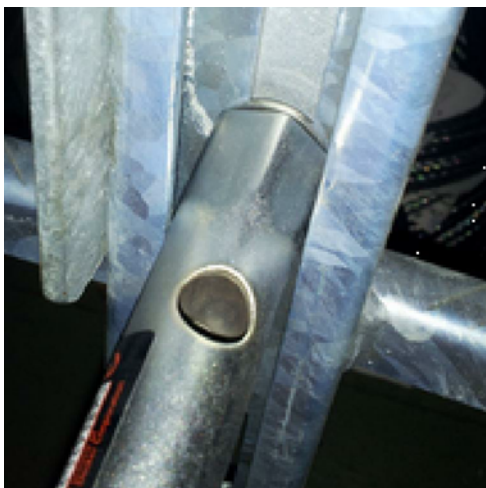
equipar a porca DIN 439 com um dispositivo de fixação de parafuso de resistência média (p. ex., Würth 08932430XX com um binário de arranque ~21 Nm) e montá-la manualmente juntamente com a anilha DIN 125, passando pelo carril desde a frente, com uma chave de caixa tubular adequada (tamanho 19)! O dispositivo de fixação de parafuso garante a necessária resistência dos freios das porcas. V. fig. 4.1
